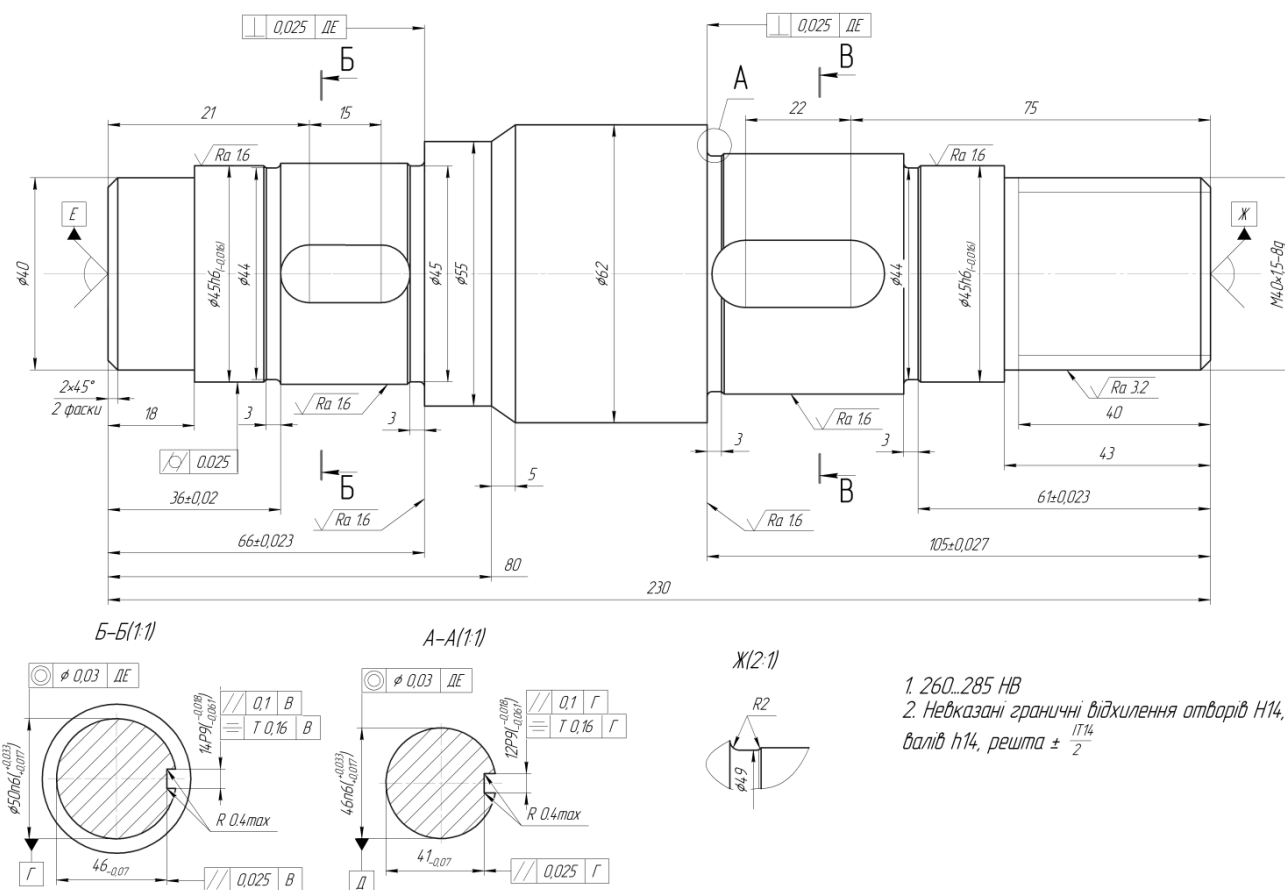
Креслення деталі «Вал 01.11»
